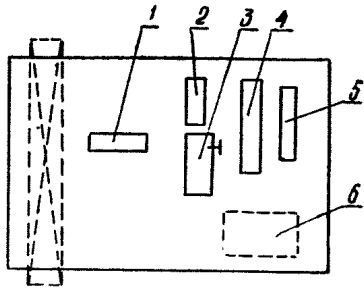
Типовая схема планировки рабочего места сборки коробки передач. 1 — пресс гидравлический; 2 — стеллаж; 3 — верстак; 4 — стенд для сборки КПП; 5 — стенд для обкатки КПП; 6 — площадка для готовой продукции
